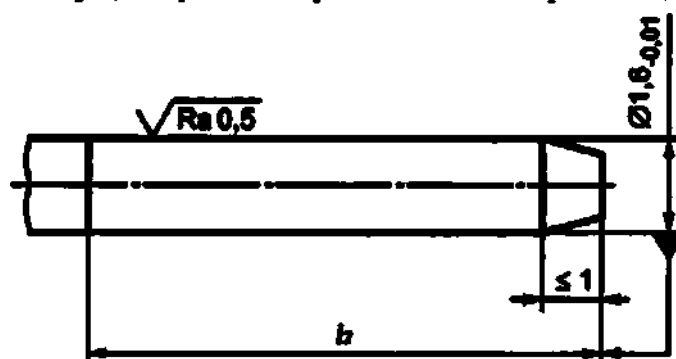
Размеры, допуски и шероховатость поверхности для хвостовика типа 3
